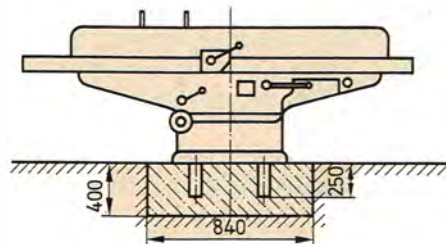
Montagezeichnung, Fundamentzeichnung einer Fräsmaschine
